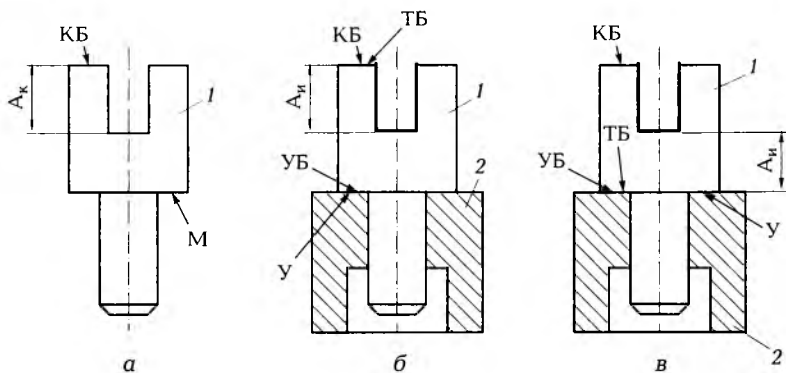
Пример использования в качестве установочной базы поверхности М обрабатываемой заготовки [а], несовмещение УБ с технологической базой [б] и совмещение УБ с технологической базой [в]:
